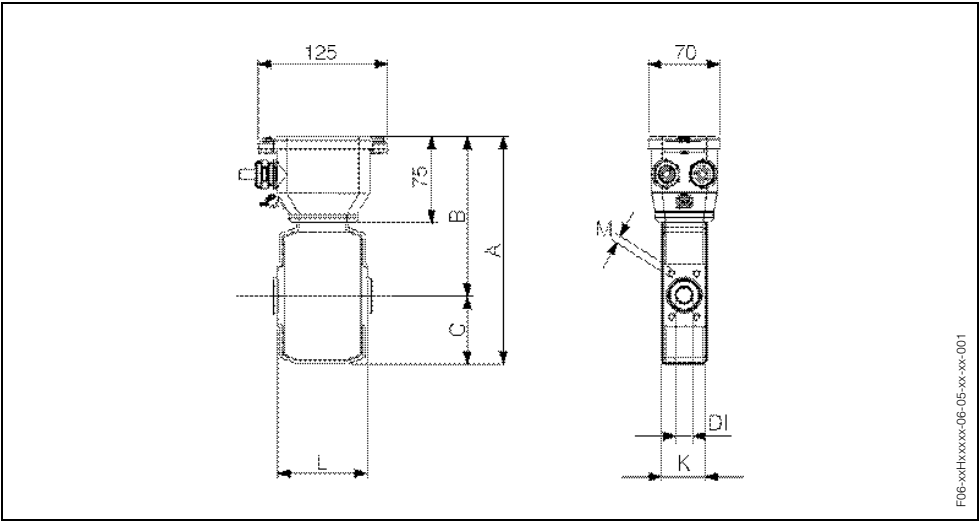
Dimensiones Promag H / DN 2...25 (versión separada)
